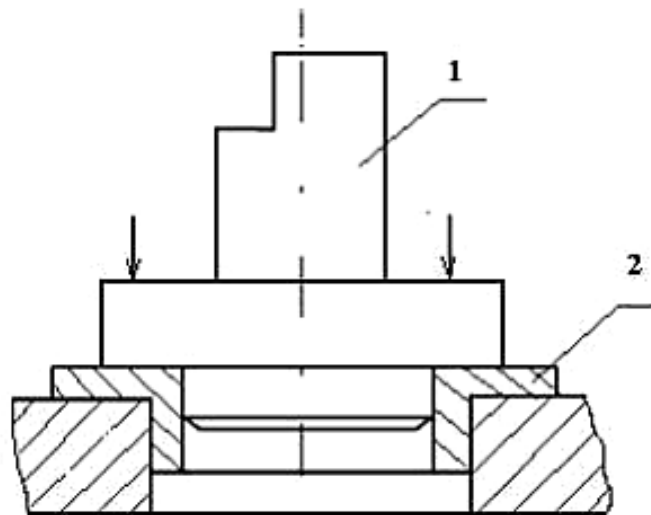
Схема установки заготовки 1 наружной цилиндрической и плоской торцевой поверхностями во втулку 2
